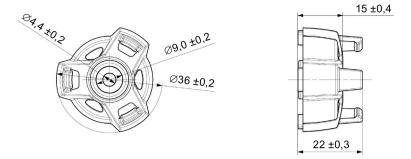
Desenho de dimensões do espaçador 6GT2690-0AK00
